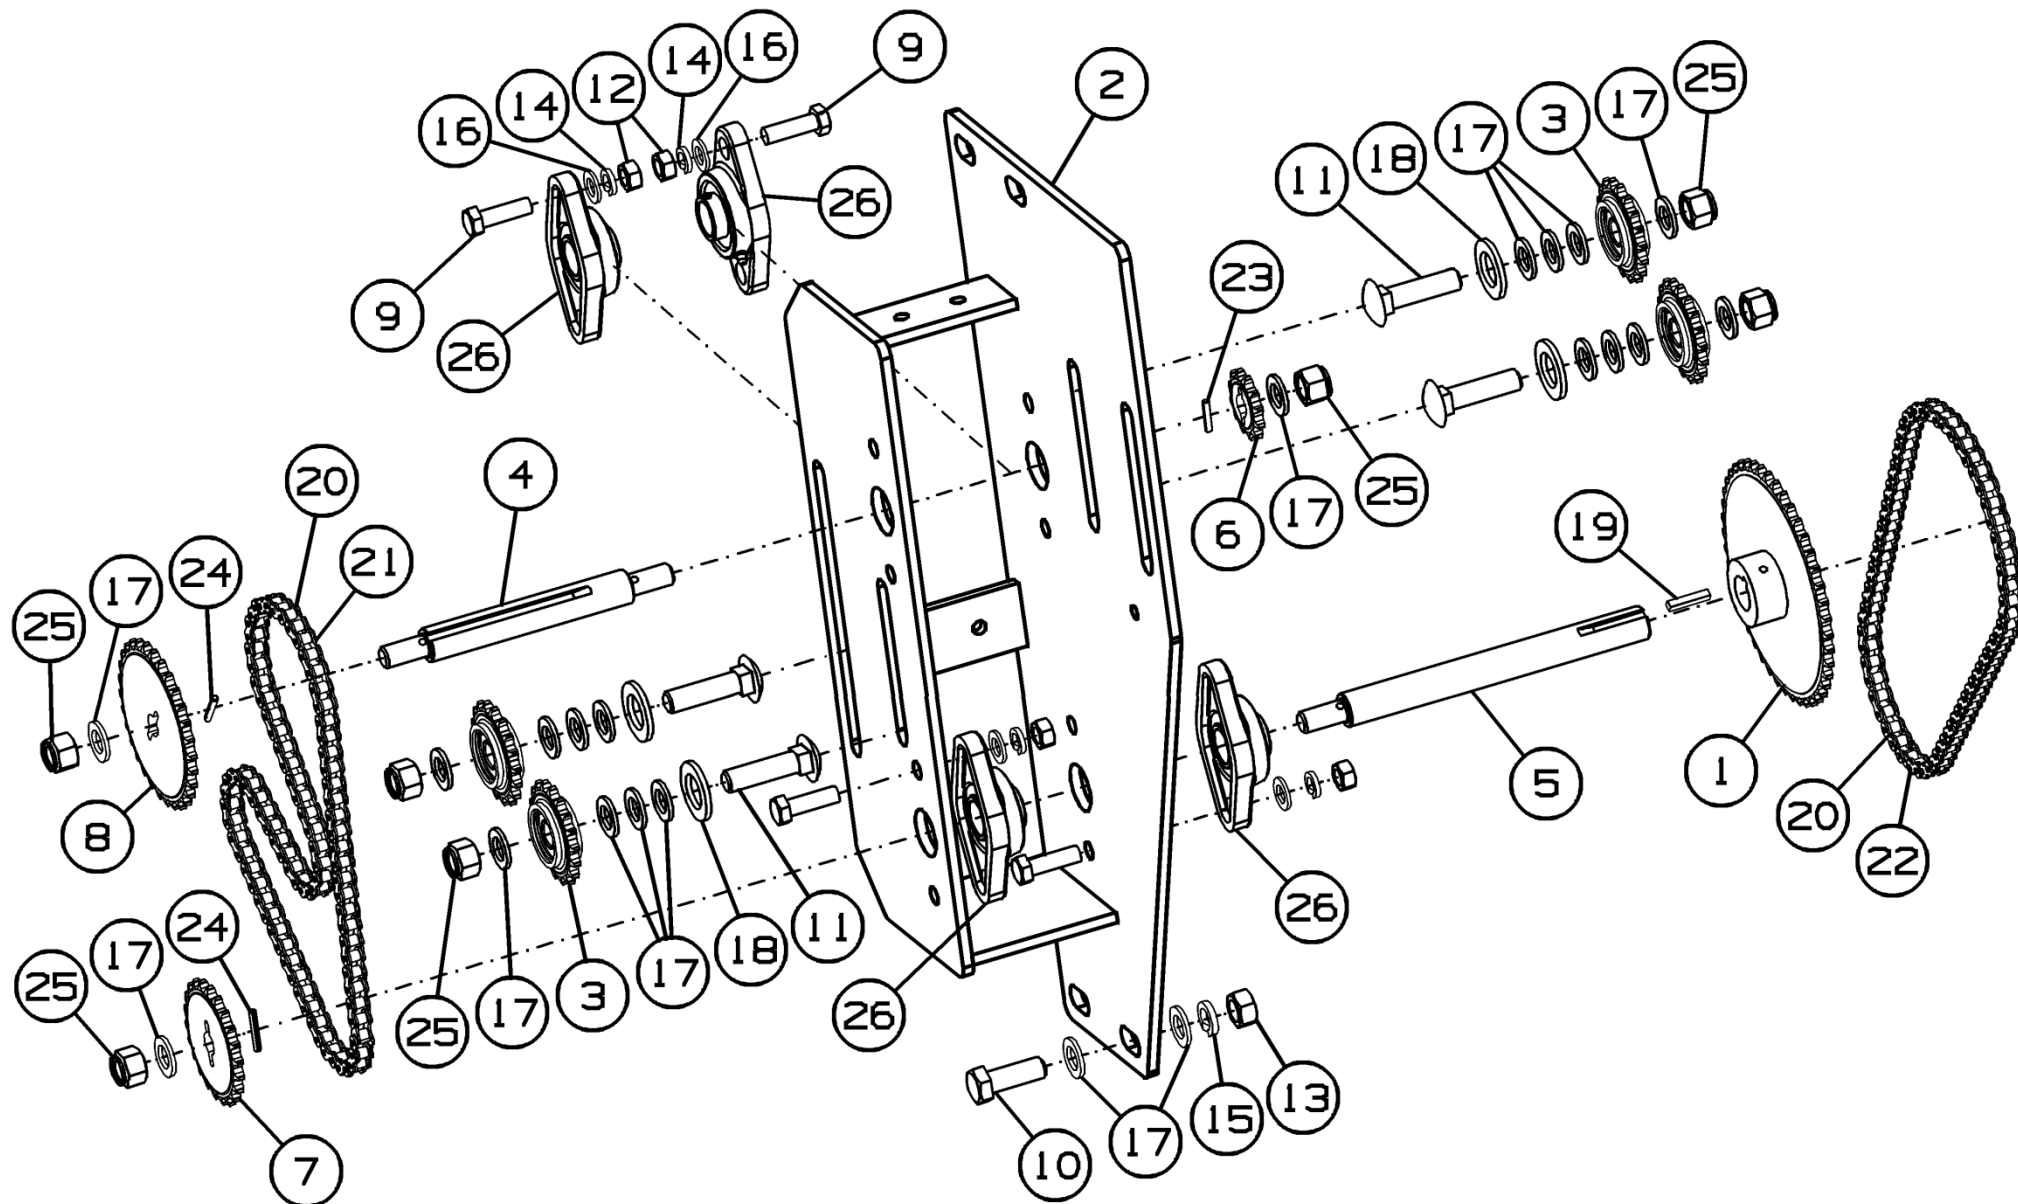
Редуктор привода АТ-11.42.300-01
